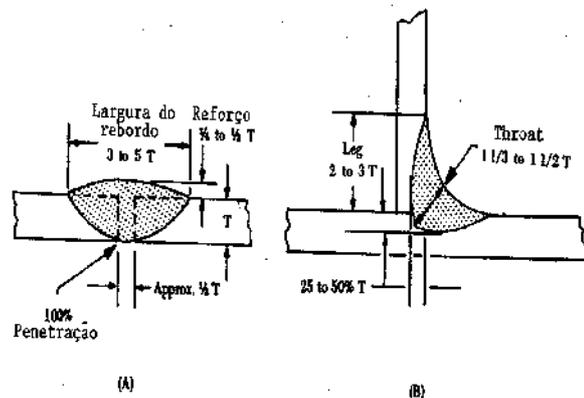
(a) solda de topo e (b) solda de filete, mostrando a largura e profundidade do rebordo.
